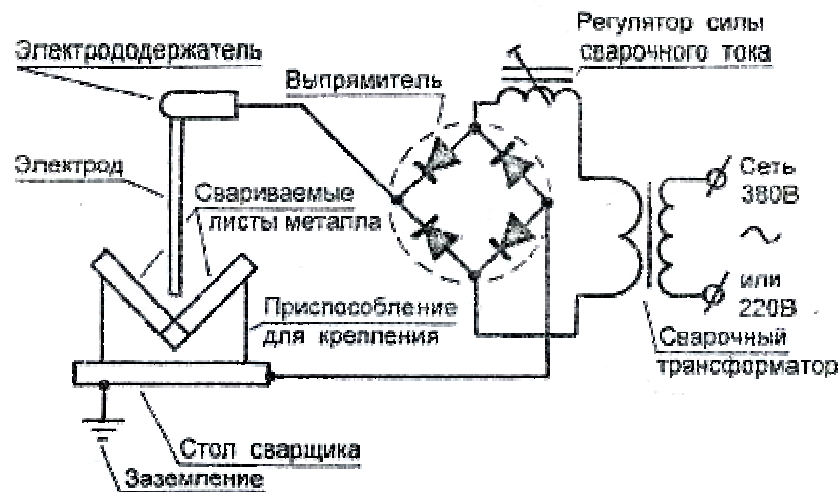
Принципиальная схема сварки выпрямленным током
